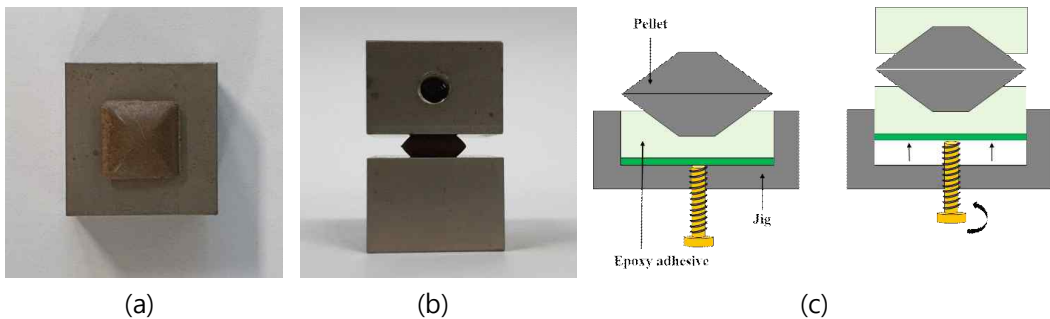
Process for surface treatment of pellet - (a) Manufactured jig, (b) Pellets between jigs, (c) Compressive strength sample
